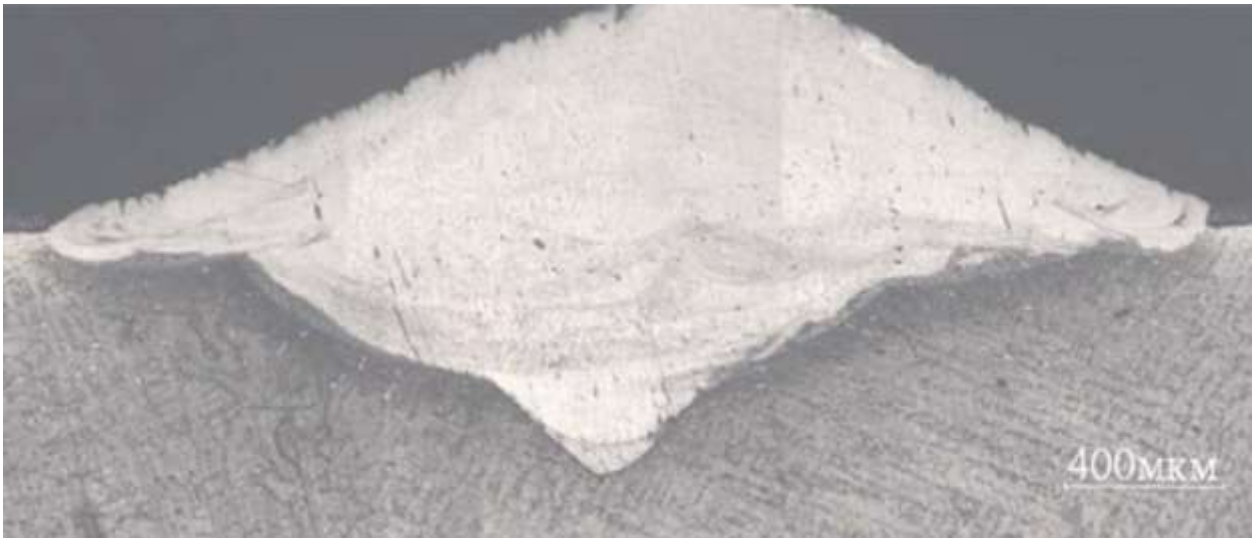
Зовнішній вигляд травленого шліфа лазерного наплавлення, виконаного за місцем ненаскрізьної тріщини
